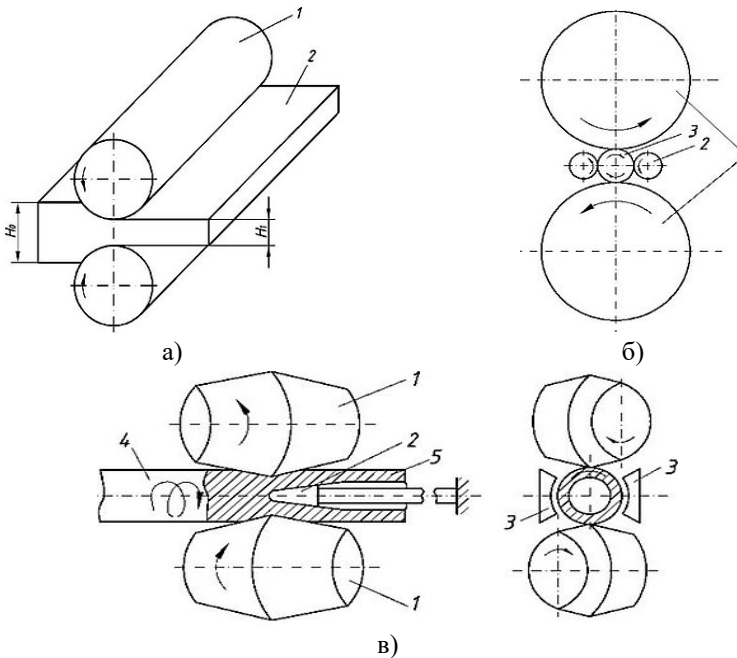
Способи прокатки: а - поздовжня: 1 – валки; 2 – заготовка-виріб; б – поперечна: 1 – валки, 2 – ролики, 3 – заготовка-виріб; в – поперечно-гвинтова: 1 – валки, 2 – оправка, 3 – лінійки, 4 – заготовка; 5 – гільза
